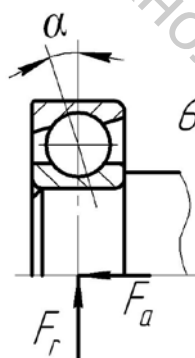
Радиально-упорный шарикоподшипник
